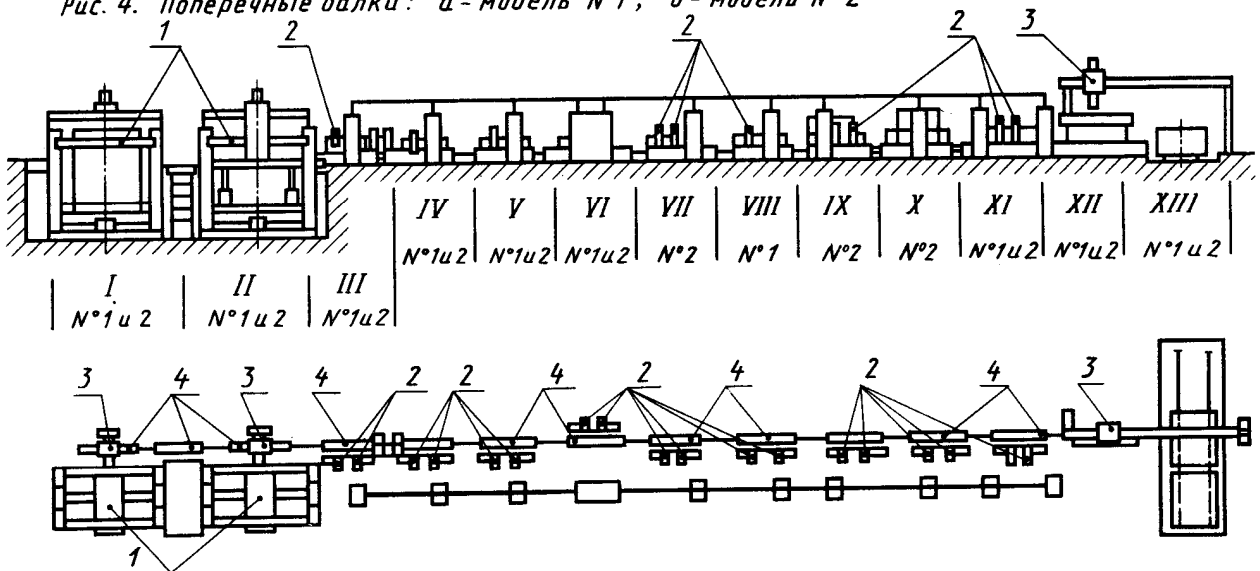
Структурная схема автоматизированной поточной линии сборки и сварки поперечных балок
